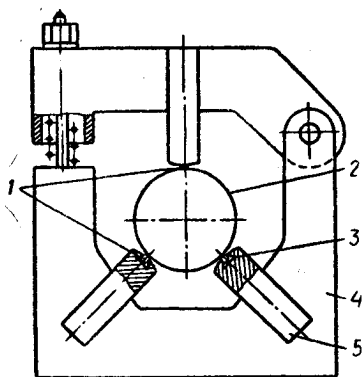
Схема кулькової обкатки зовнішньої циліндричної поверхні:
